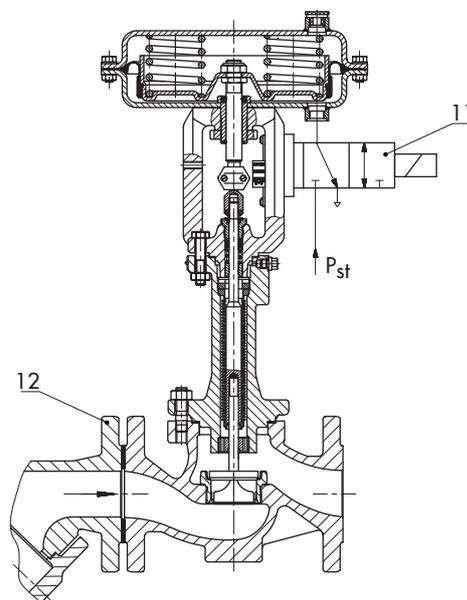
Автоматический запорный клапан Тип 3241-1-газ
